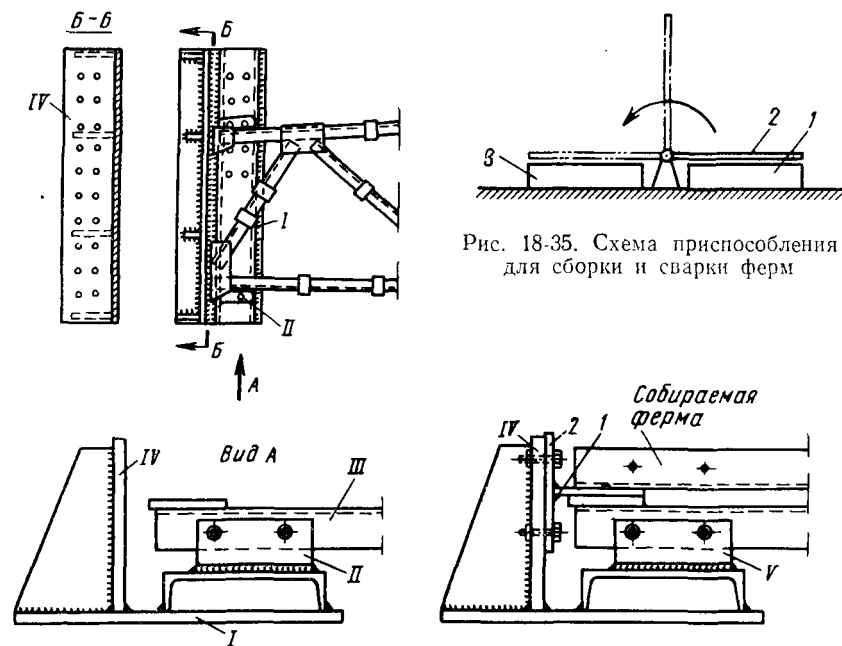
Схема приспособления для сборки и сварки ферм
